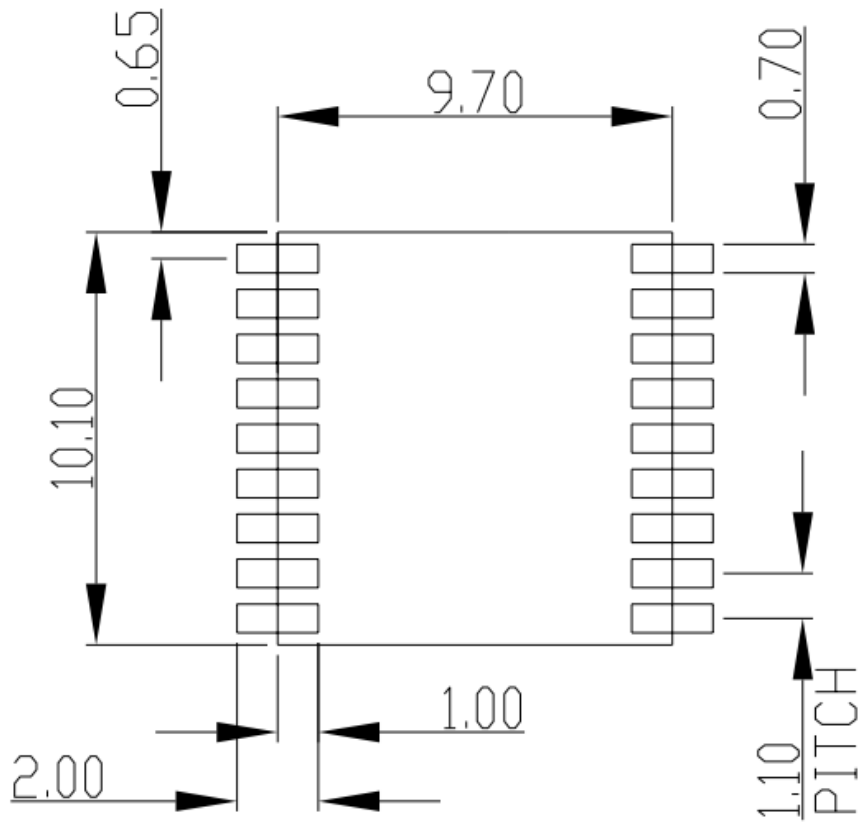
PCB 推荐封装 (顶视图) (Unit: mm)
